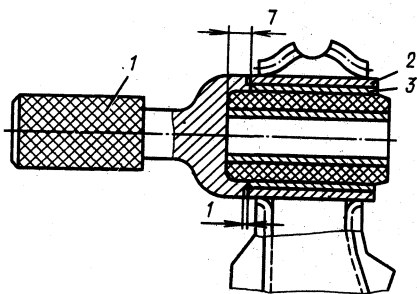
Запрессовка резино-металлических шарниров в рычаг задней подвески автомобиля «Запорожец»:
